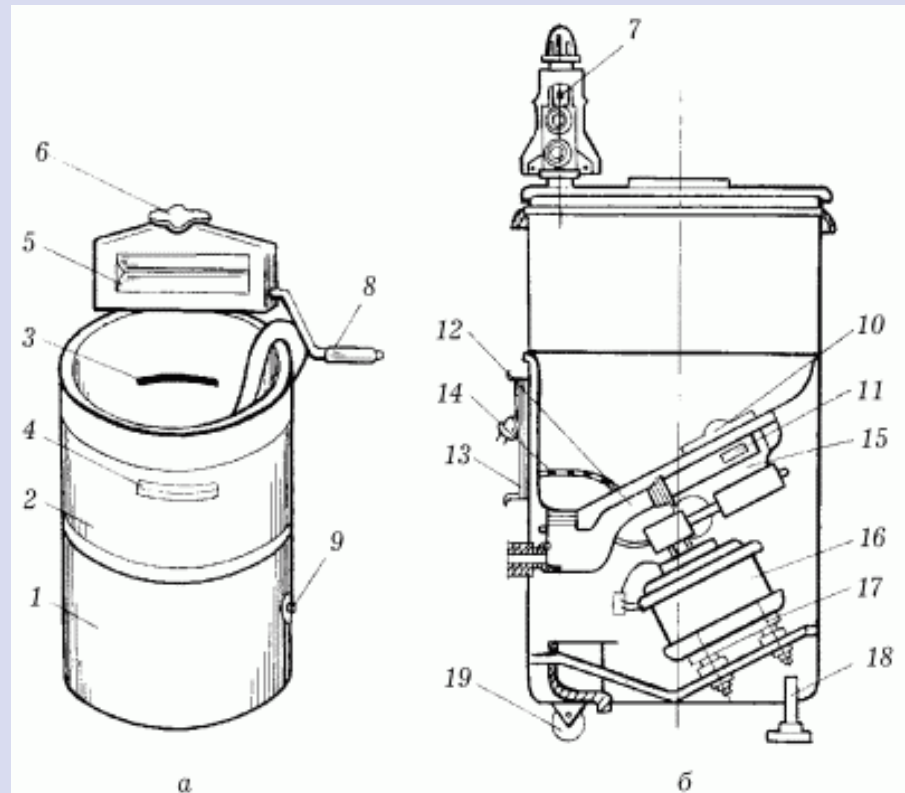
Устройство стиральной машины типа СМР: а – общий вид; б – продольный разрез; 1 – корпус; 2 – стиральный бак; 3 – уровень заполнения бака водой; 4 – ручка; 5 – валики ручного отжима; 6 – регулировочный винт отжима; 7 – пружина; 8 – рукоятка отжимного устройства; 9 – реле; 10 – активатор; 11, 12 – сливной и соединительные шланги; 13 – шнур; 14 – решетка; 15 – насос; 16 – электродвигатель; 17 – рама; 18 – скоба для удержания машины при отжиме; 19 – ролик.
